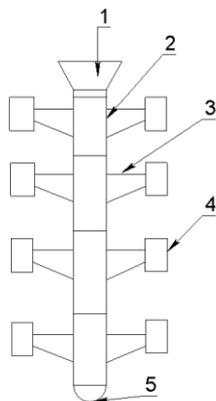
Блок отливок: 1- литниковая чаша; 2- стояк; 3- питатели; 4- отливки; 5- зумпф.
